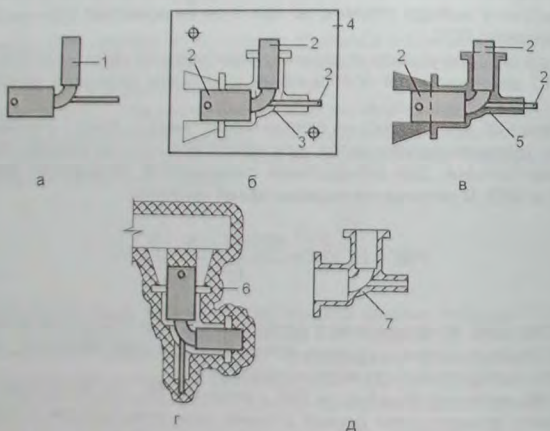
Этапы выполнения в отливке внутренних полостей с помощью стержня: 1 – стержень керамический (графитовый); 2 – знаковая часть стержня; 3 – рабочая полость пресс-формы; 4 – пресс-форма; 5 – модель отливки со стержнем; 6 – КО (ГО); 7 – отливка
